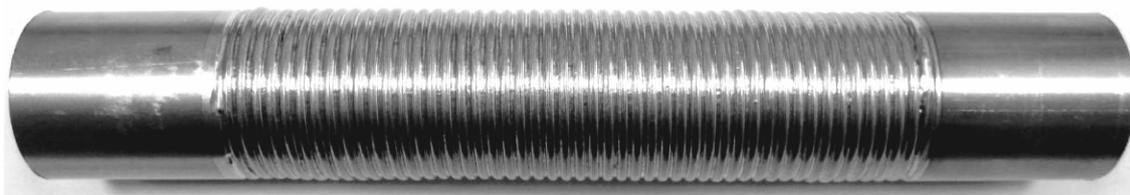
Внешний вид образца-свидетеля пружинно-витого канала
